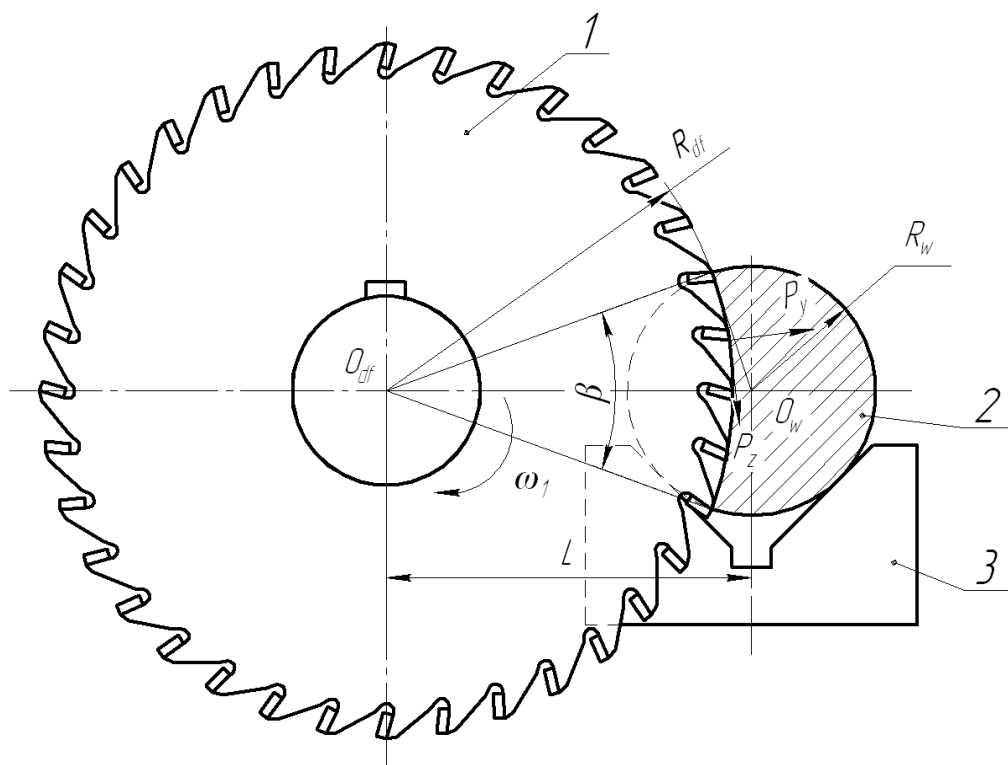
Розрахункова схема геометричних параметрів процесу різання циліндричної заготовки дисковою фрезою: 1 – дискова фреза; 2 – циліндрична заготовка; 3 – призма
